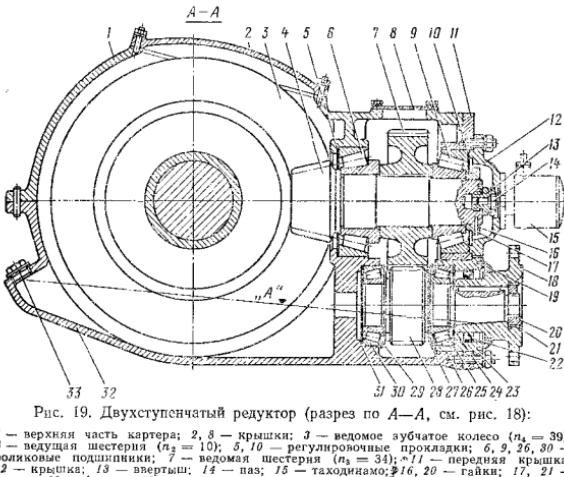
Двухступенчатый редуктор (разрез по 4-4, см. рис. 18):
